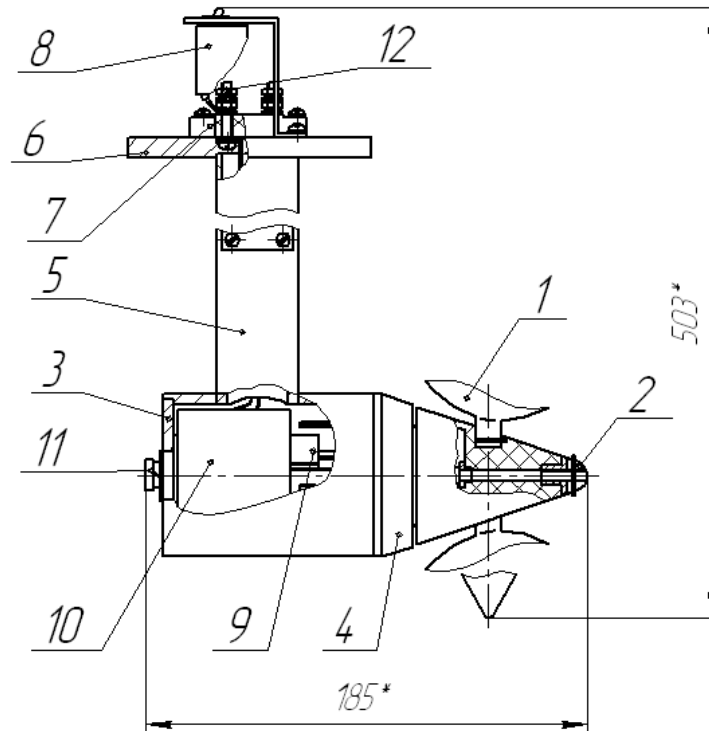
Датчик скорости воздуха (1 - крыльчатка; 2 - гайка; 3 - обойма; 4 - корпус; 5 - труба; 6 - фланец; 7 - контактная площадка; 8 - микротумблер; 9 - ротор; 10 - блок; 11 - болт; 12 - шпилька)
